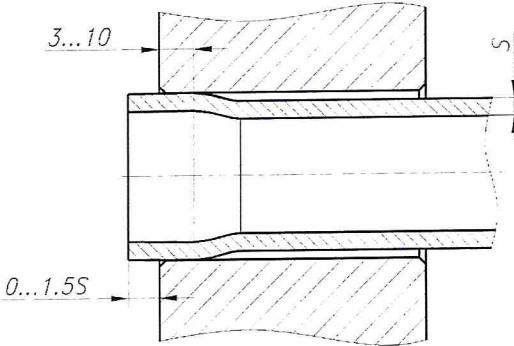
б – Развальцовка труб цилиндрической вальцовкой перед сваркой
